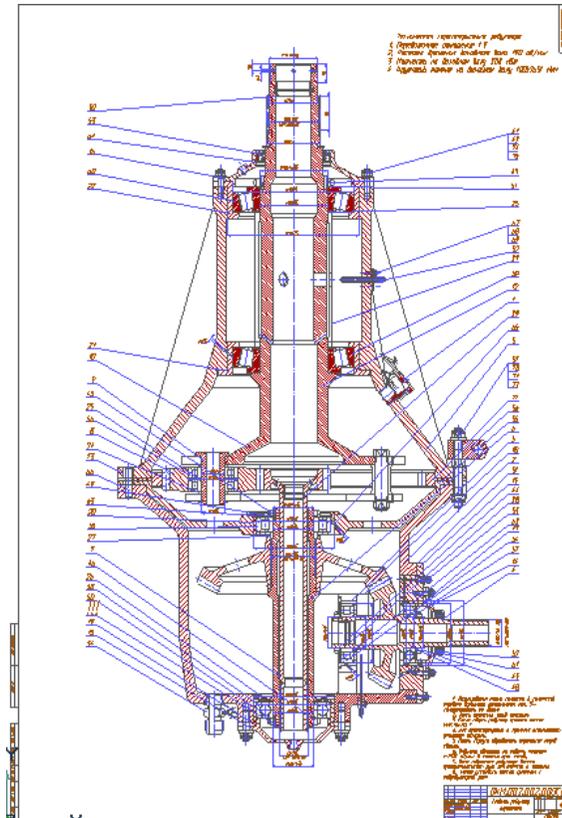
Сборочный чертеж редуктора (главный вид)
